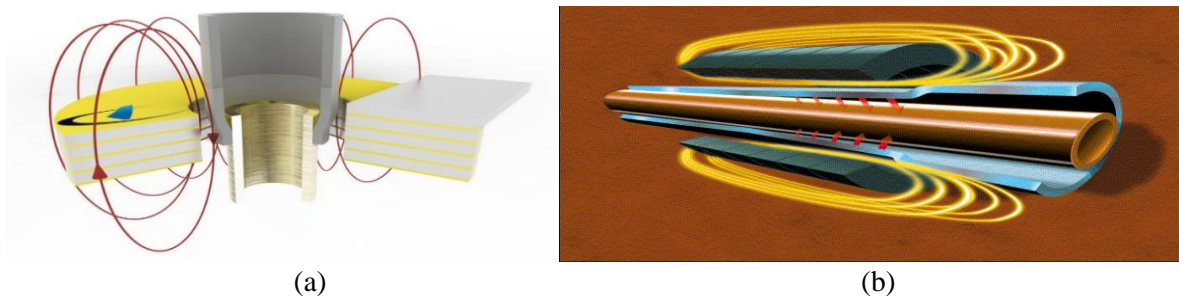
Le champ magnétique généré par la bobine lors du soudage de tubes [5]
